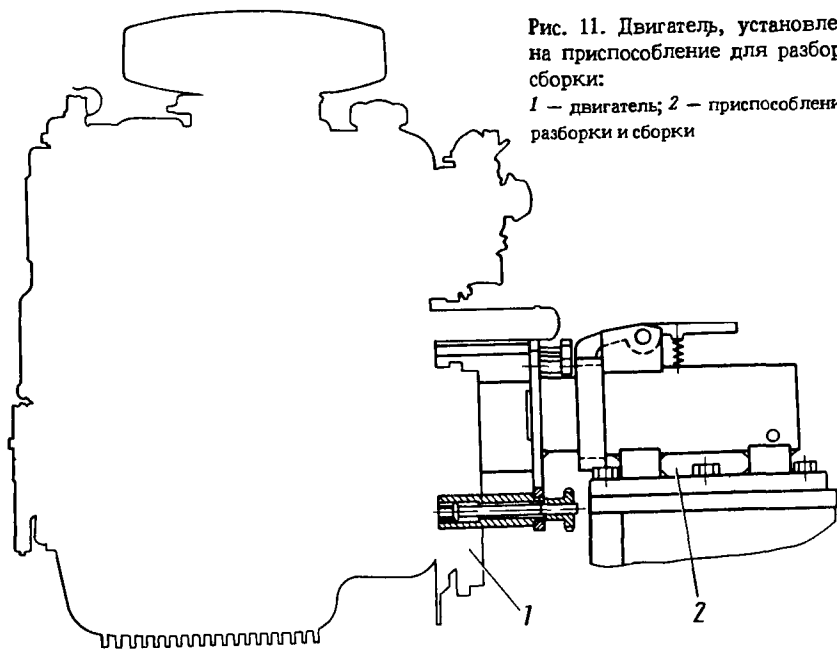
Двигатель, установленный на приспособление для разборки и сборки:
